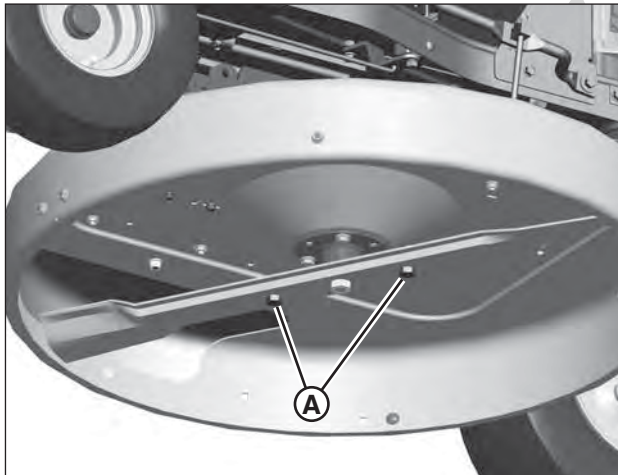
Vérifier le couple de serrage de boulon de montage de lame
